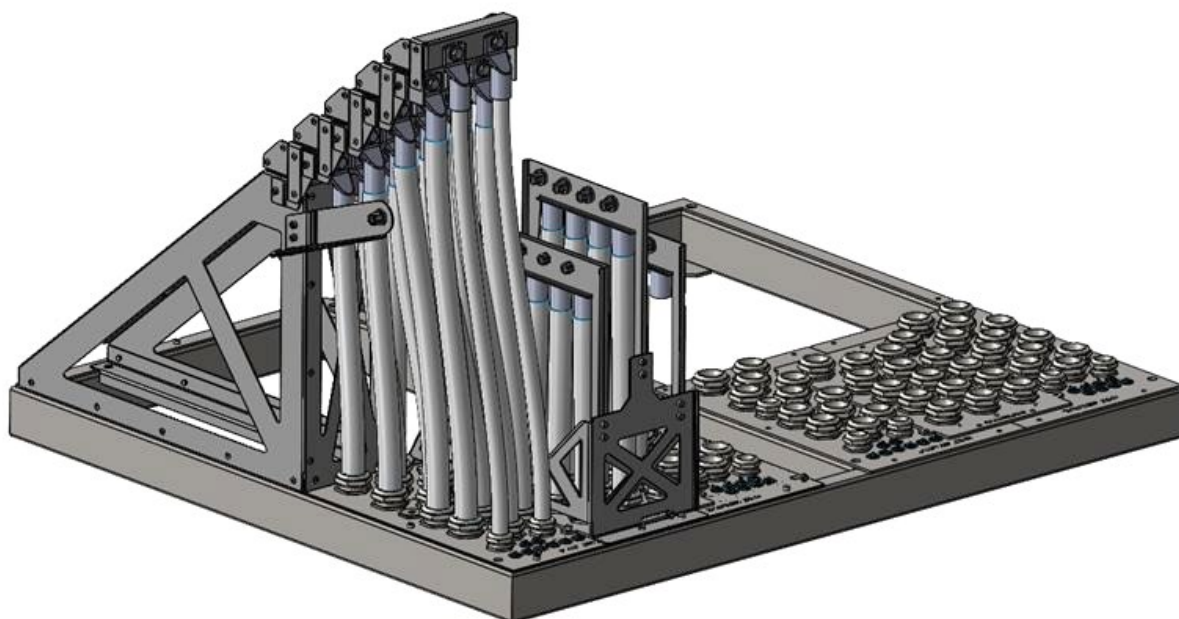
Am Cable Jig angebrachtes DC-Kabel
